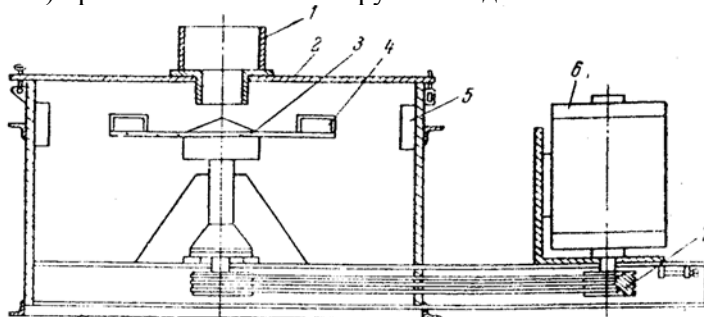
Дробилка «Торнадо». 1 – питающая труба; 2 – крышка корпуса; 3 – ротор; 4 – разгонные ребра; 5 – отбойные плиты; 6 – электродвигатель; 7 – клиноременная передача.
